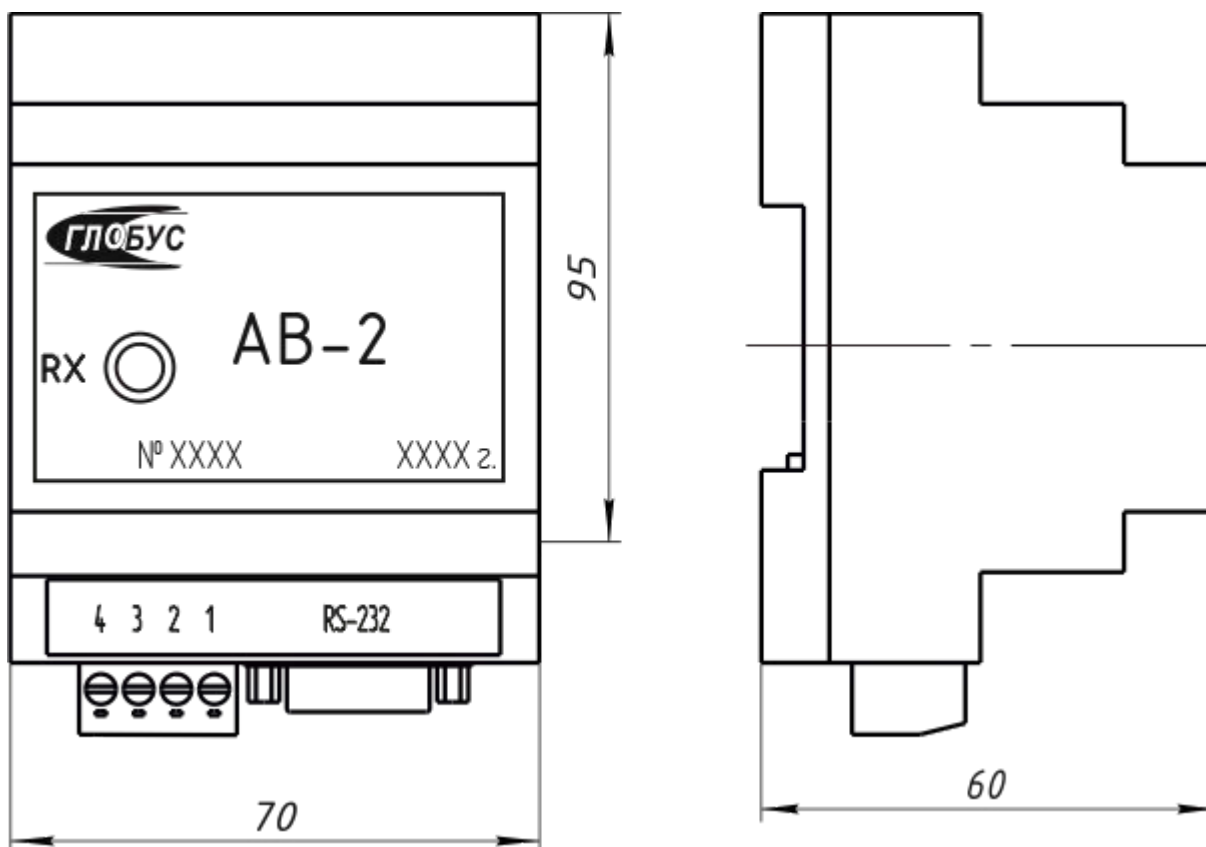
Габаритный чертеж блока «АВ-2»
